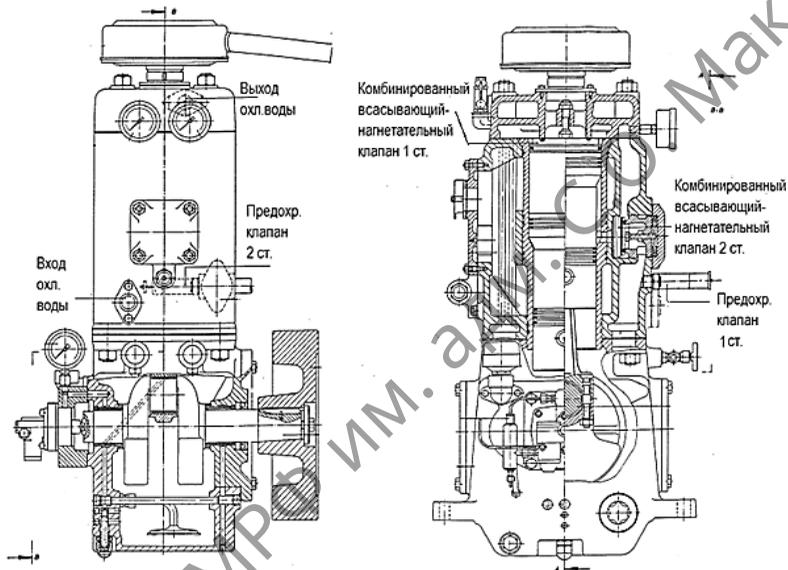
Компрессор фирмы Хатлапа тип W140
